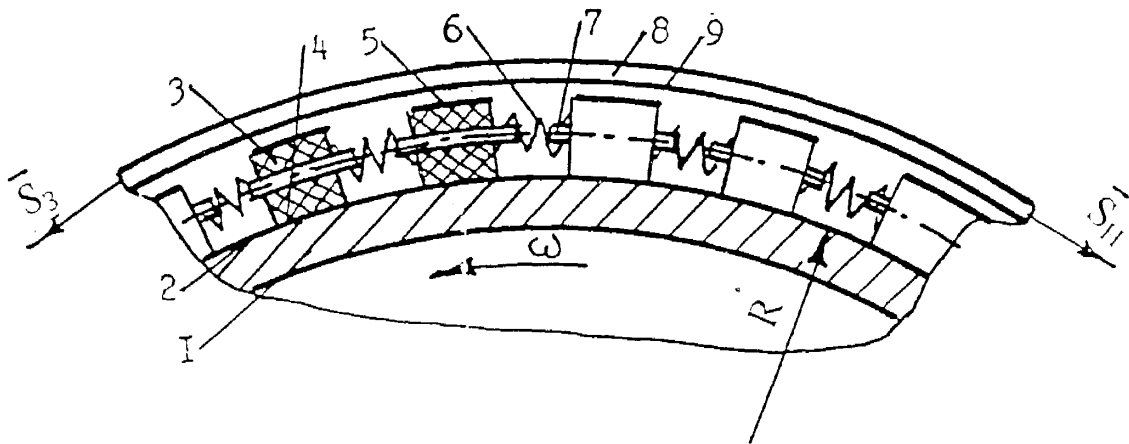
Схема стрічково-колодкового гальма з рухомими накладками: 1, 2 – гальмівний шків та його робоча поверхня; 3, 4, 5 – фрикційна накладка з внутрішньою та зовнішньою поверхнями; 6 – циліндрична пружина; 7 – стрижень; 8, 9 – гальмівна стрічка з робочою поверхнею
